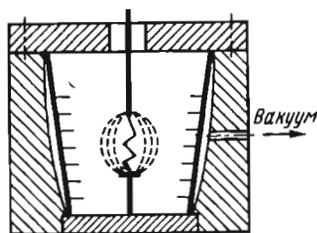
Технологический блок для электрогидравлической штамповки из кольцевых и трубчатых заготовок
